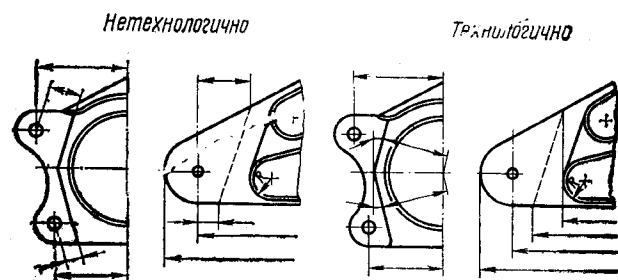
Простановка размеров на детали типа ушка (вилки).
